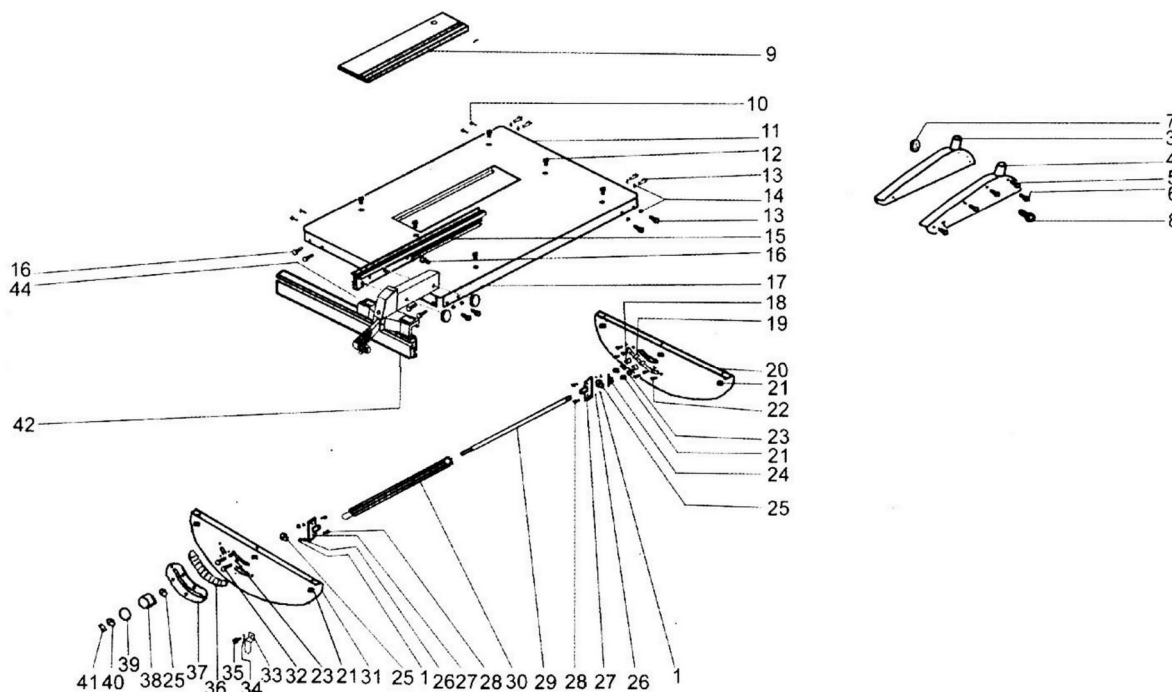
Vista explodida — mesa, guias e mecanismo de inclinação
